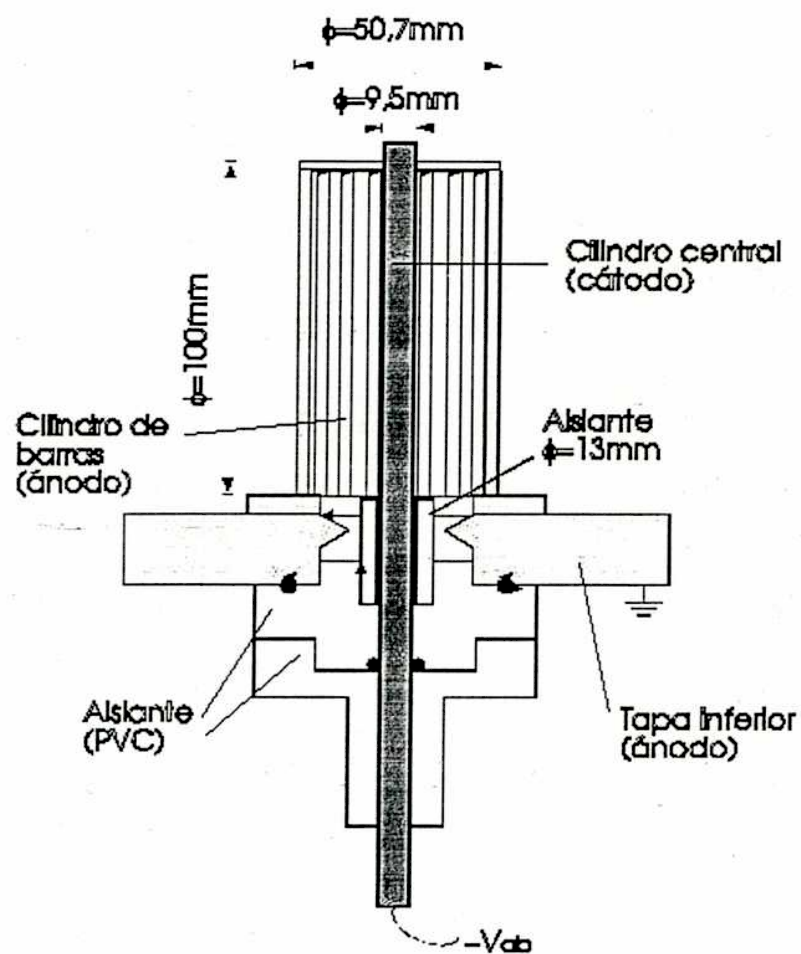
Detalle de los electrodos, el aislante y piezas auxiliares del equipo CCII.
